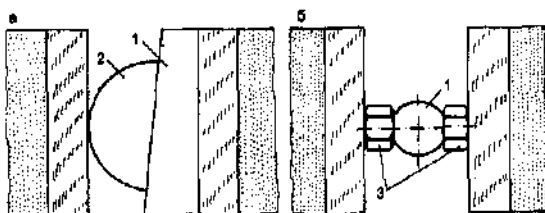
Фиксация в тисках детали призматической (а) и шаровидной (б) формы: 1 — деталь; 2 — полуцилиндрическая прокладка; 3 — гайки
